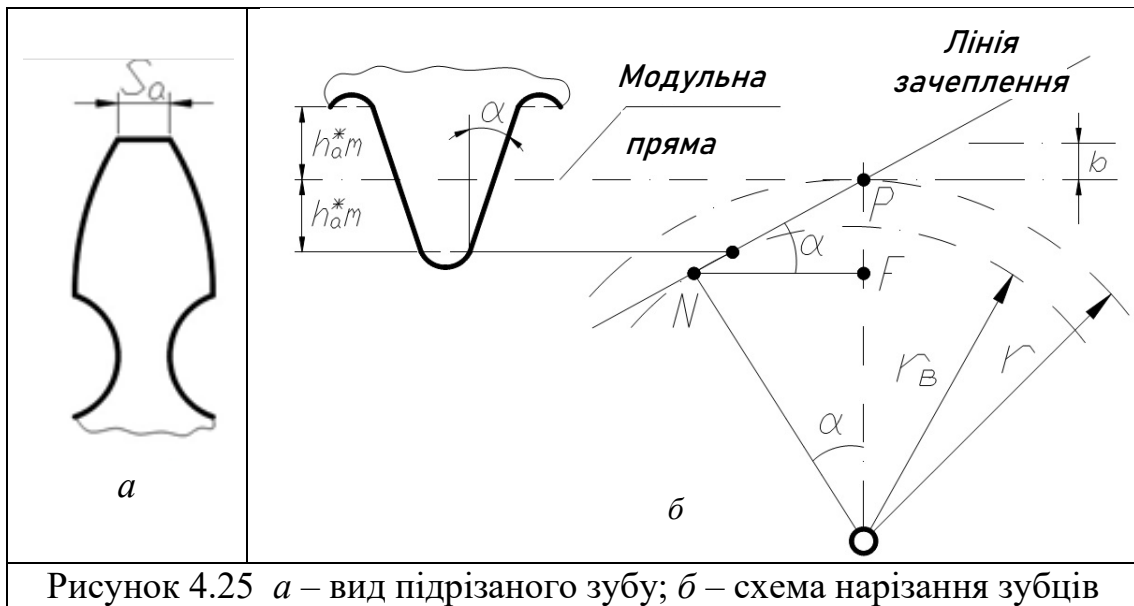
а – вид підрізаного зуба; б – схема нарізання зубців
